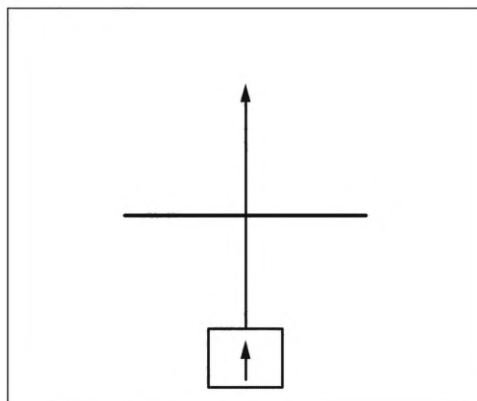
Движение преобразователя для получения опорного сигнала
